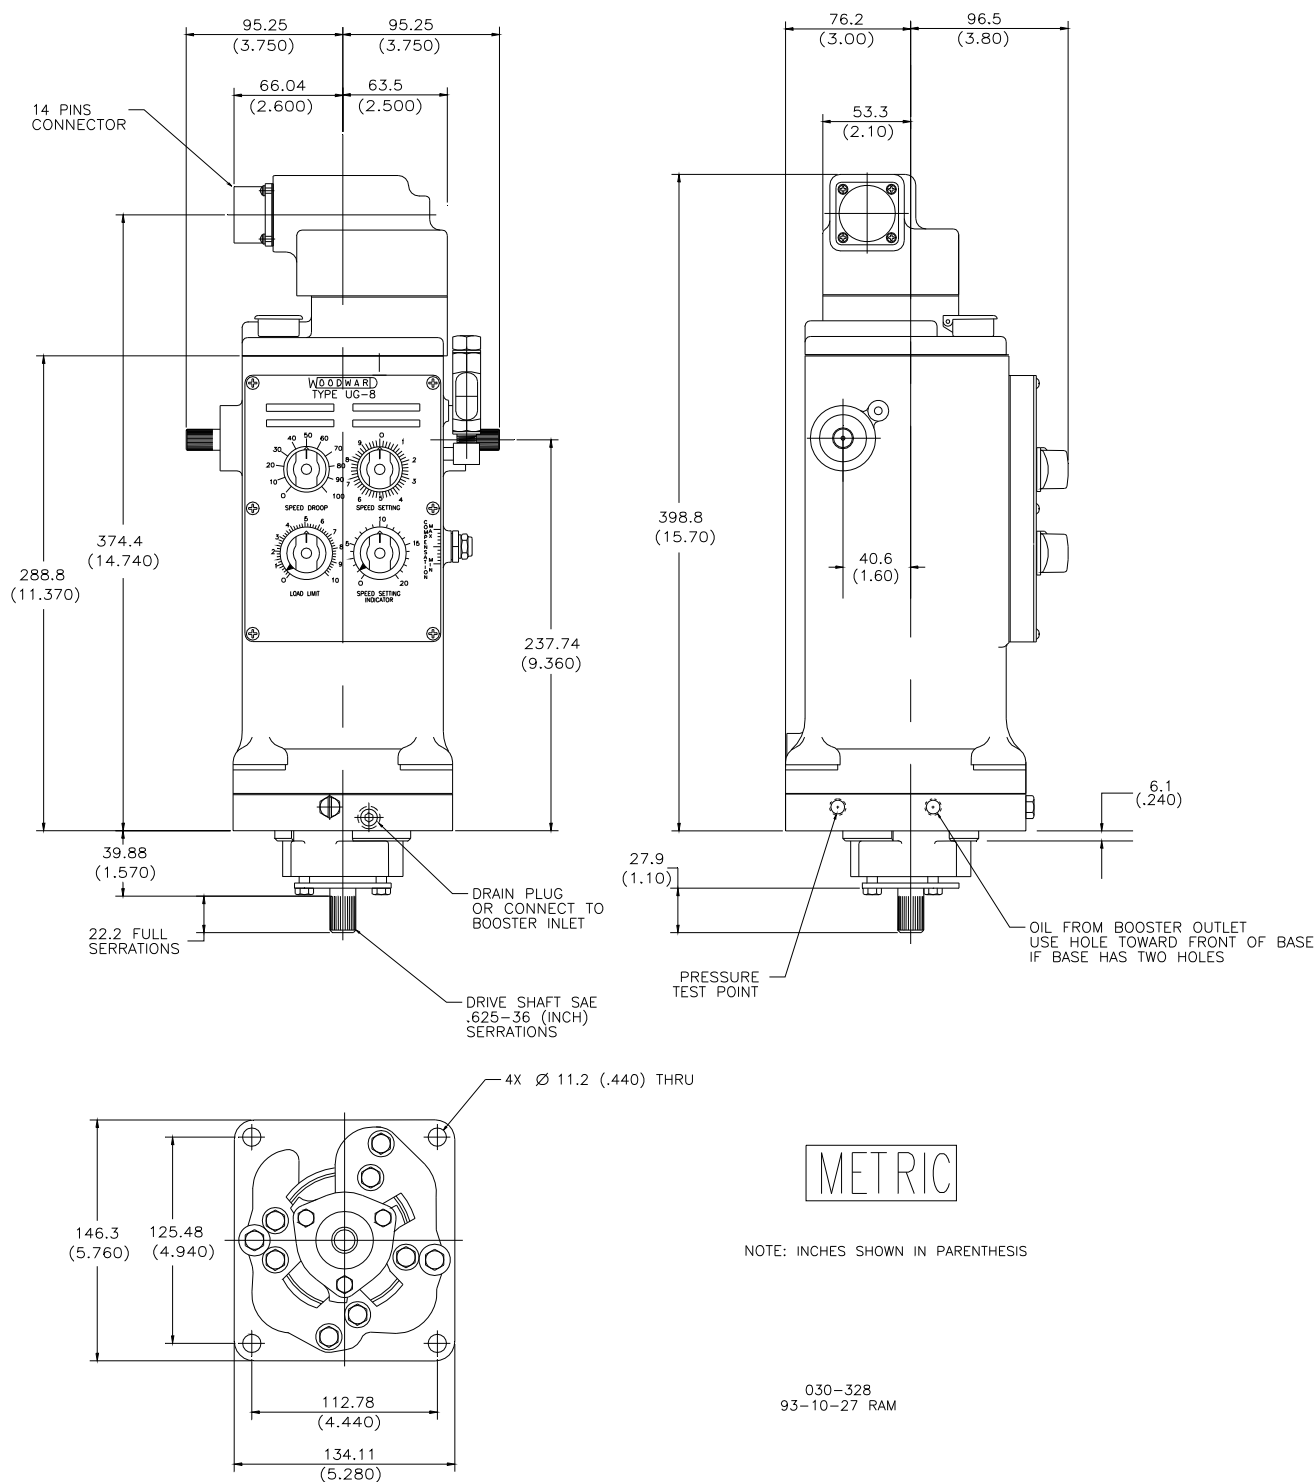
典型 UG-8D MAS 调速器的外观尺寸
